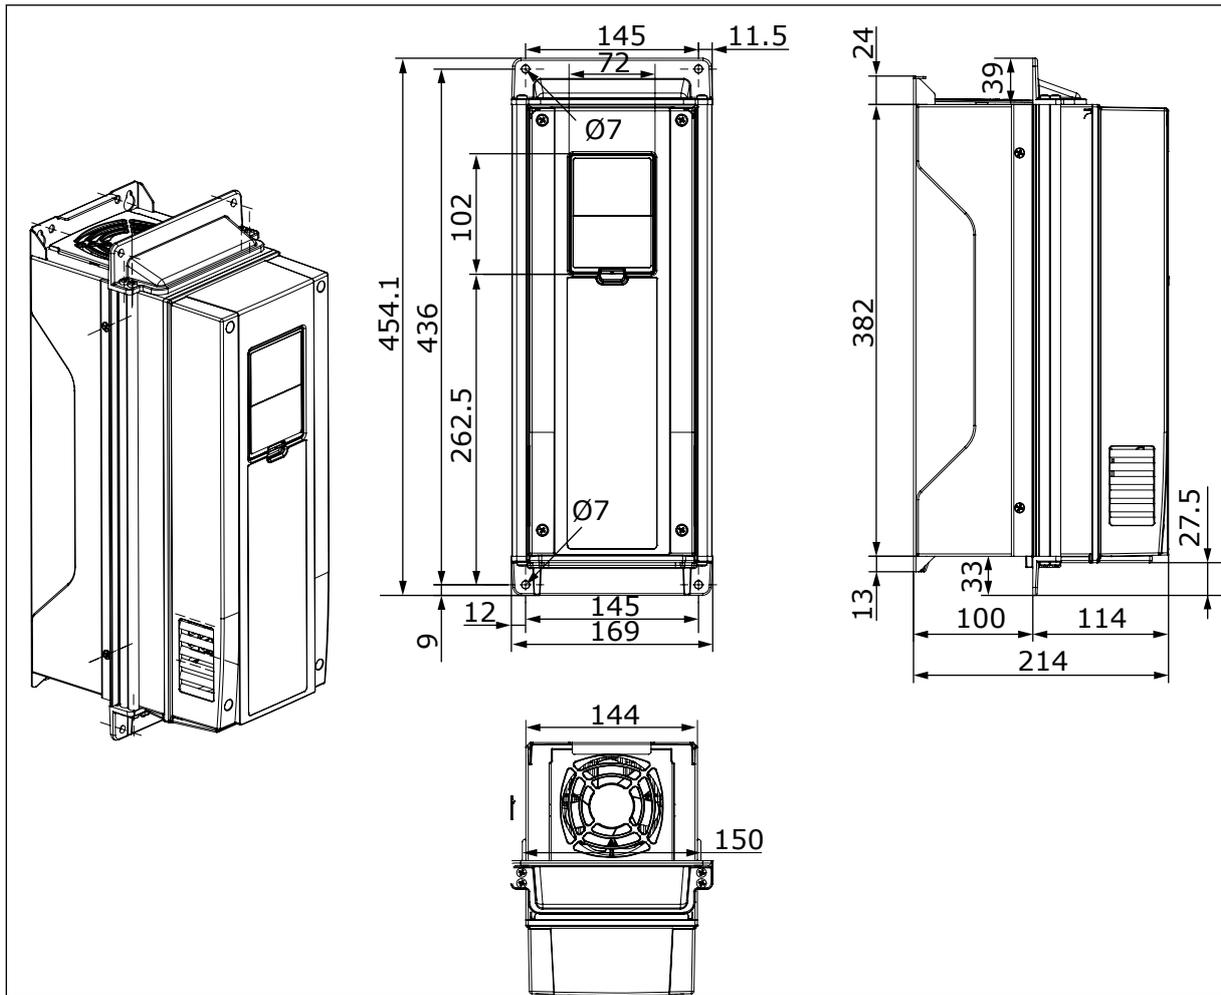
Abmessungen des Frequenzumrichters, Flanschbefestigung, MR5 [mm]
